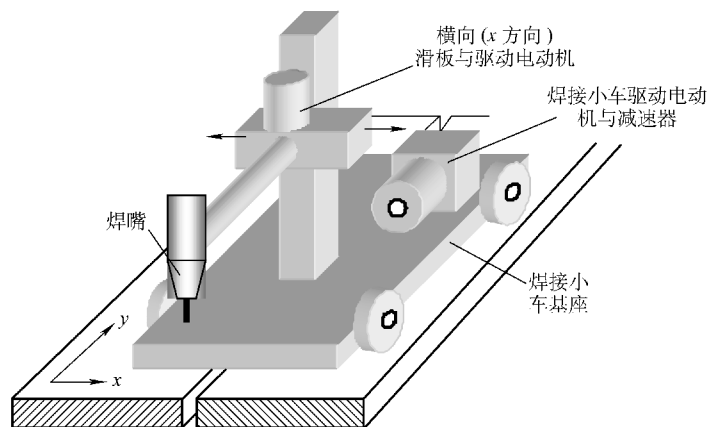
焊接小车一般实现平面焊缝跟踪
